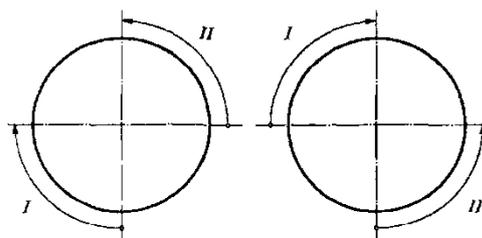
Порядок наложения корневого слоя шва при сварке вертикального неповоротного стыка двумя сварщиками
